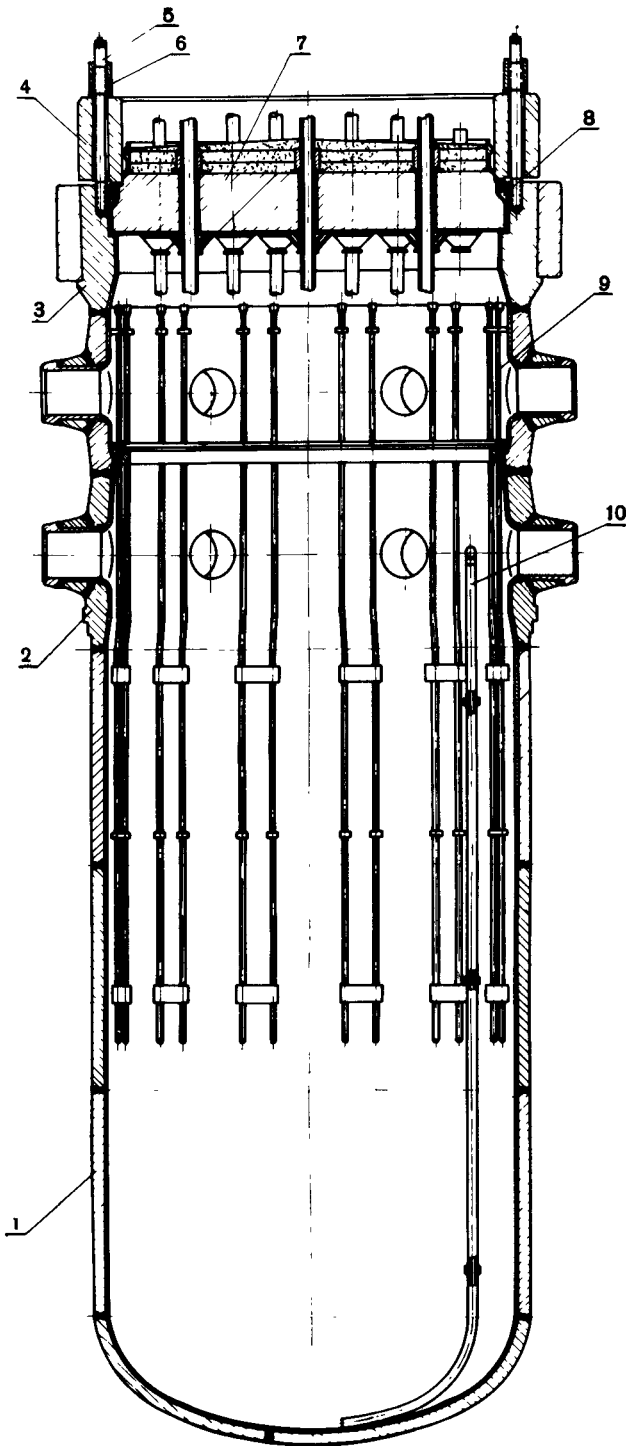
Корпус реактора Нововоронежской АЭС: 1 — нижняя зона; 2 — средняя зона; 3 — верхняя зона; 4 — нажимное кольцо; 5 — шпилька; 6 — гайка; 7 — крышка; 8 — клиновидная прокладка; 9 — каналы под загрузку образцов корпусной стали; 10 — труба продувки и опорожнения
